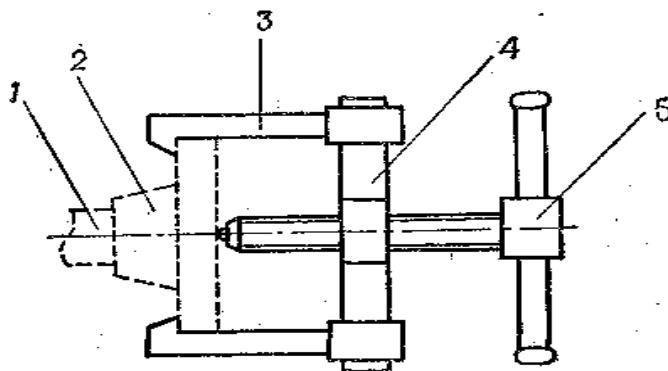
Съемник: 1 – вал электродвигателя; 2 – полумуфта; 3 – захват; 4 – траверса; 5 – винт
